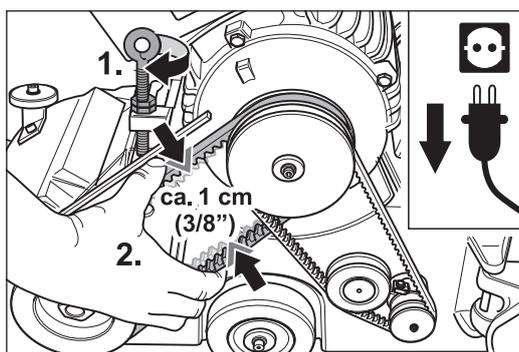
Zum Spannen des Antriebsriemens die Ringschraube am Motor im Uhrzeigersinn drehen (1.).
